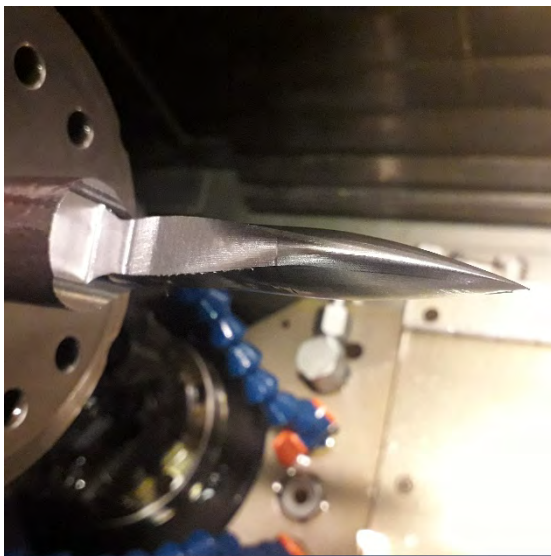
Чистовое фрезерование оставшейся второй части поверхности
